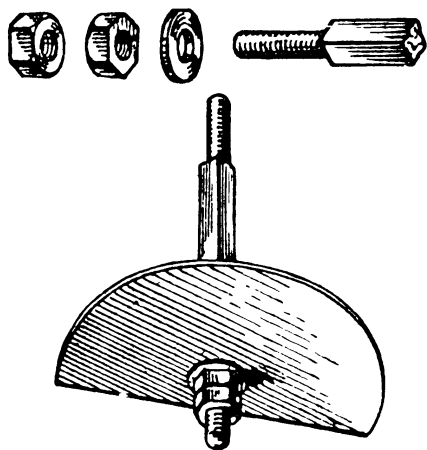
Четырехгранный шпиндель для вращающейся части конденсатора вместе с гайками и шайбами.
